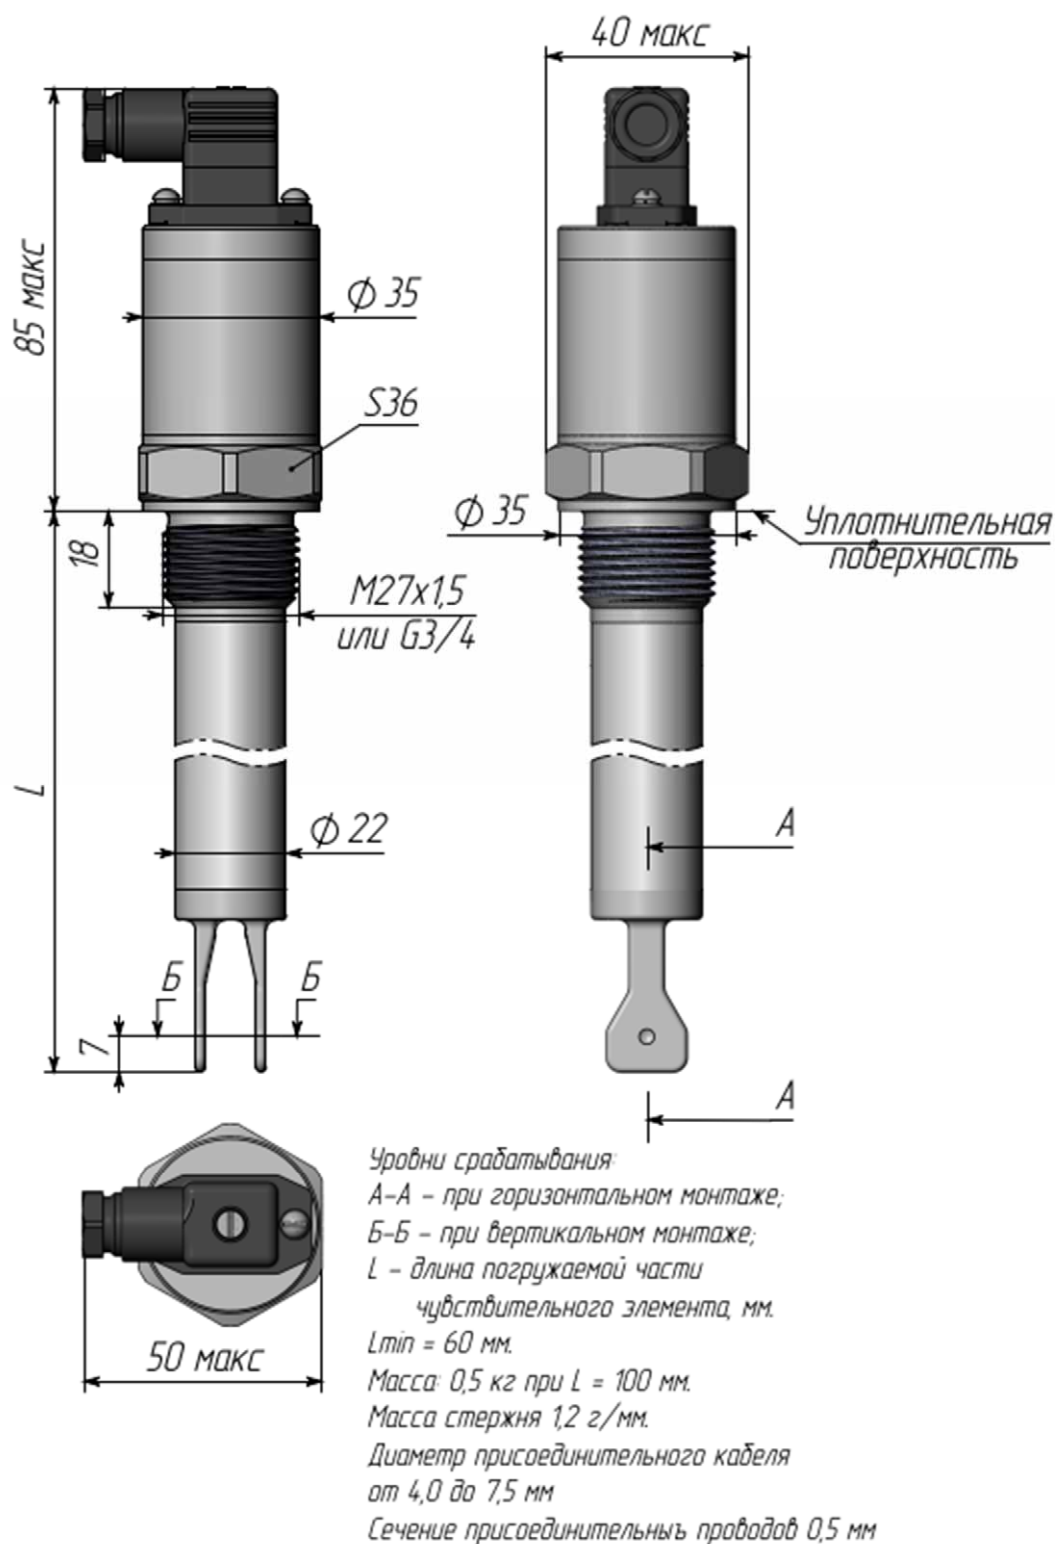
Габаритные и установочные размеры малогабаритного сигнализатора уровня ВИБРОТЭК-У-М-В со способом присоединения штуцер G3/4, M27x1,5(2), K3/4", R3/4
